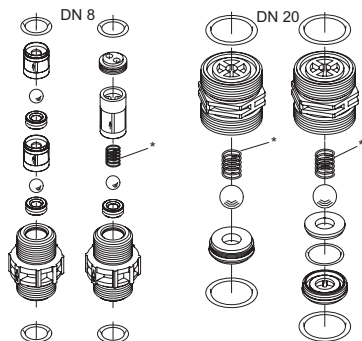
Клапан из нержавеющей стали или пластмассы DN 8 / DN 20, * подпружиненный (опция)
